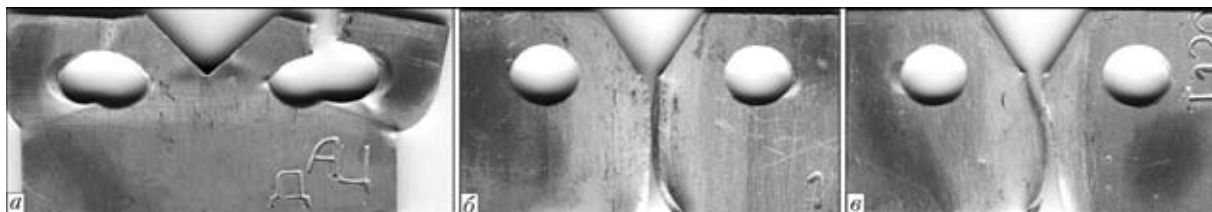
Внешний вид разрушенных образцов основного материала (а) и сварных соединений сплава АМцН, полученных способом АДСНЭ (б) и СТП (в)
